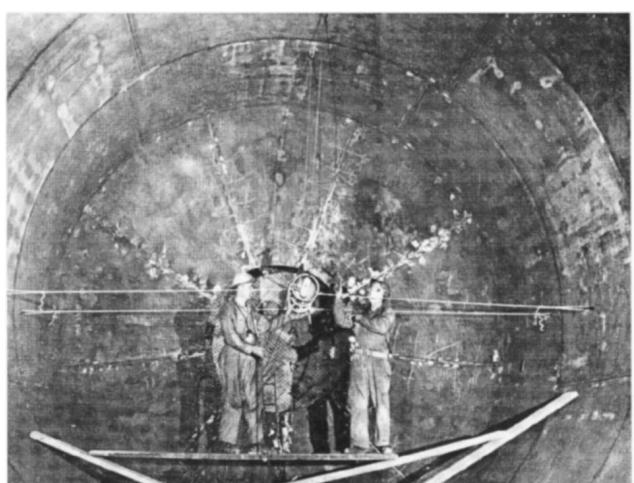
Установка рентгеновского источника на оси бака. Снаружи бака за каждым сварочным швом находилась рентгеночувствительная пленка для контроля качества сварки. (*Острые грани*, июнь 1966 г.)
